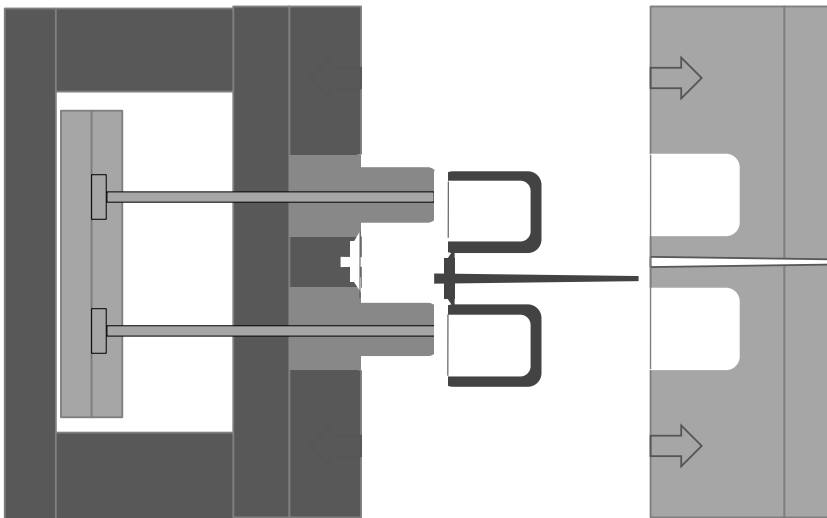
Becherwerkzeug mit Punktanguss – geöffnet
